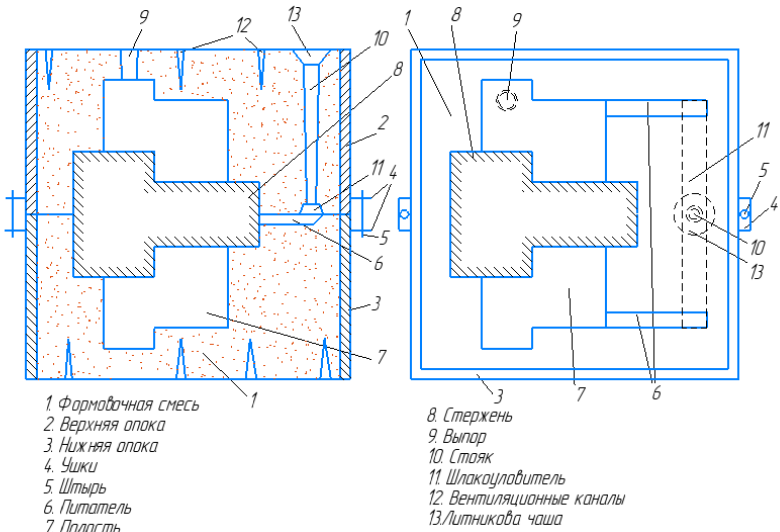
Литейная форма в сборе (эскиз) для формовки детали «штуцер» по варианту № 1 с горизонтальным расположением стержня (слева – основной вид, справа – вид сверху)
